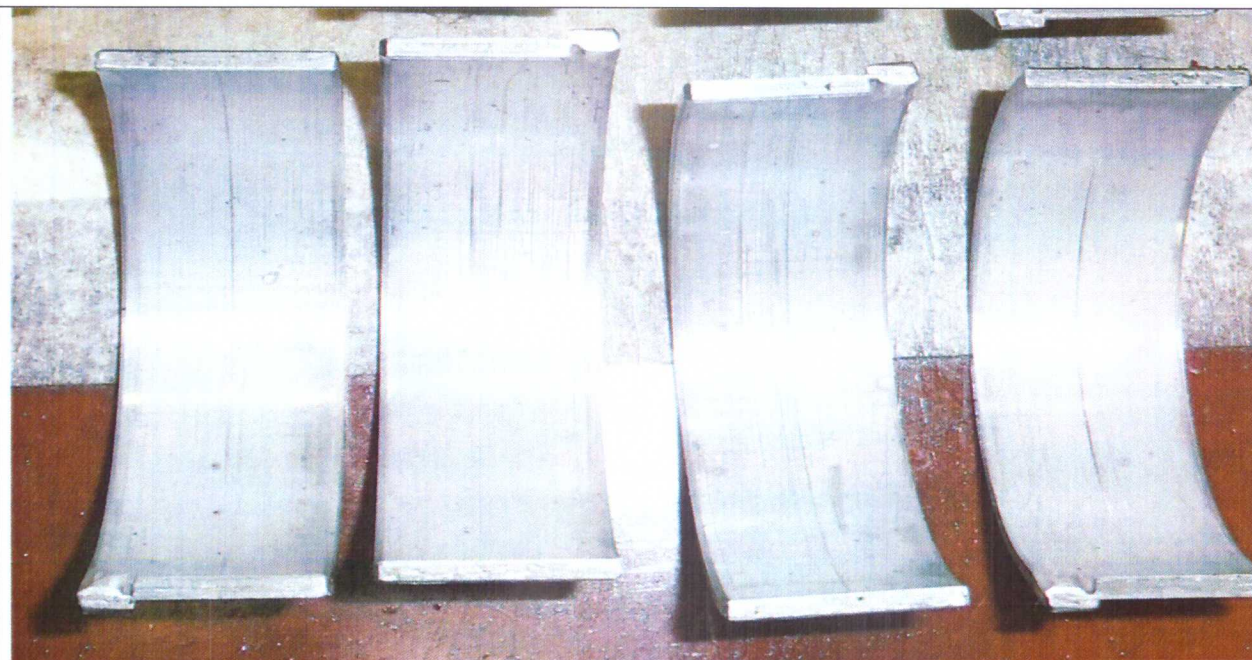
Внешний вид рабочей поверхности нижних вкладышей шатунных подшипников коленчатого вала по окончании длительных испытаний двигателя при работе на базовом масле Castrol EDGE с добавкой нанокompозита Amortect PROOF
